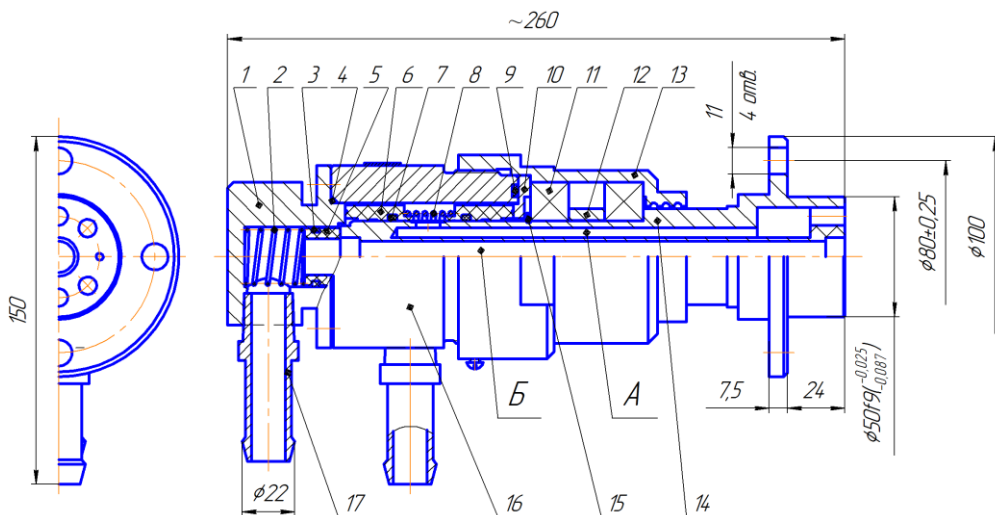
Вертлюжок сдвоенный БНГ.102.00.00
